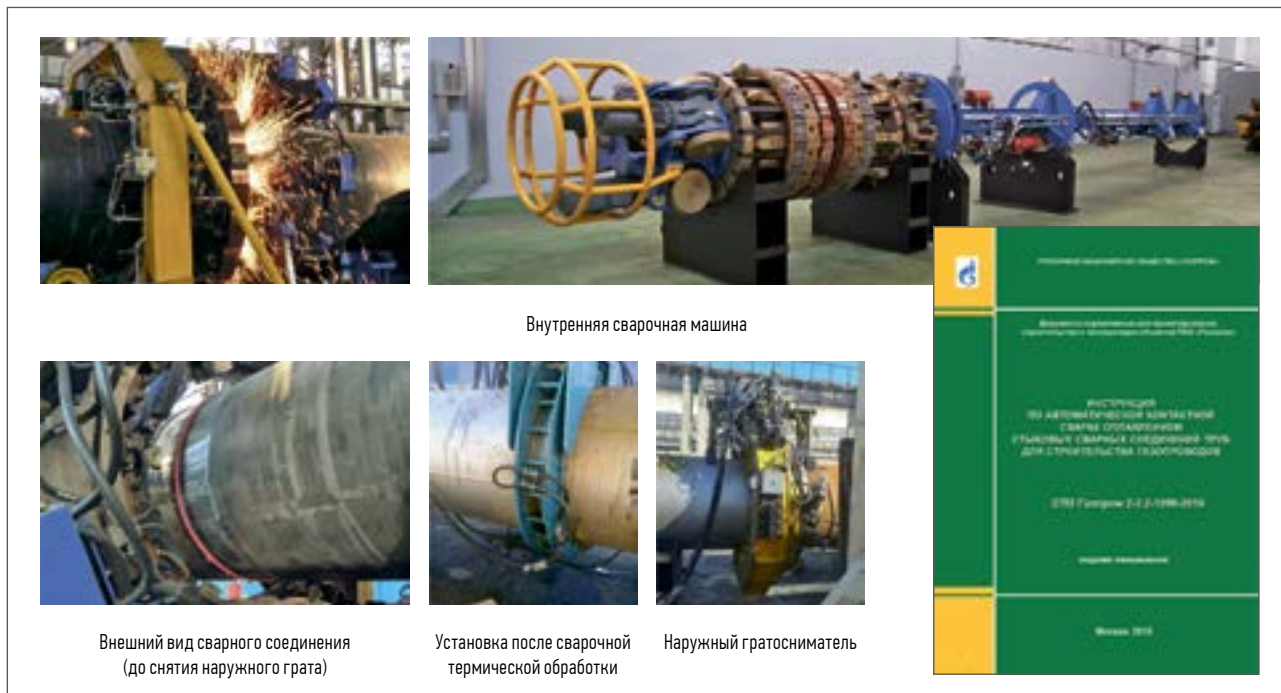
Комплекс автоматической контактной стыковой сварки оплавлением (КСО) труб большого диаметра от DN 1000 до DN 1400 российского производства
